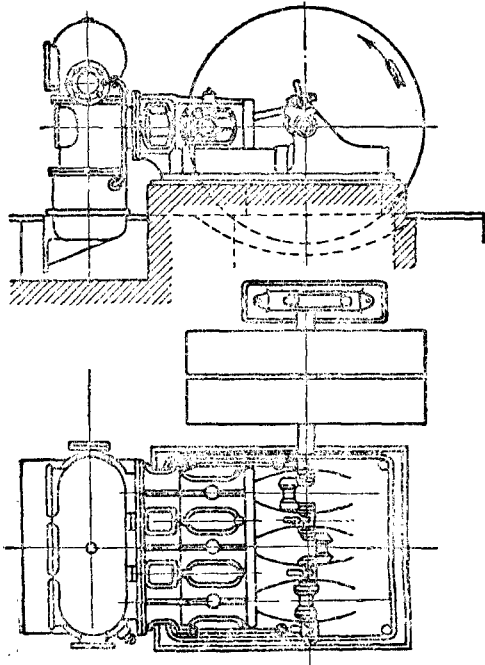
Одноцилиндровый насос двойного действия с зубчатой передачей
